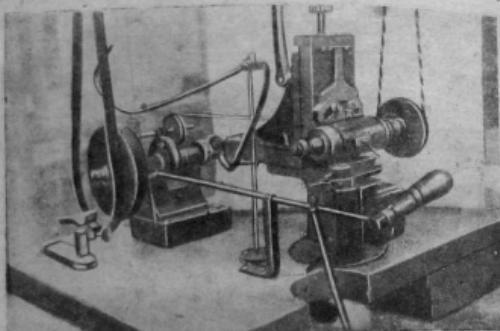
Станок Салаз для фрезеровки пазов в платинках и мостиках.
